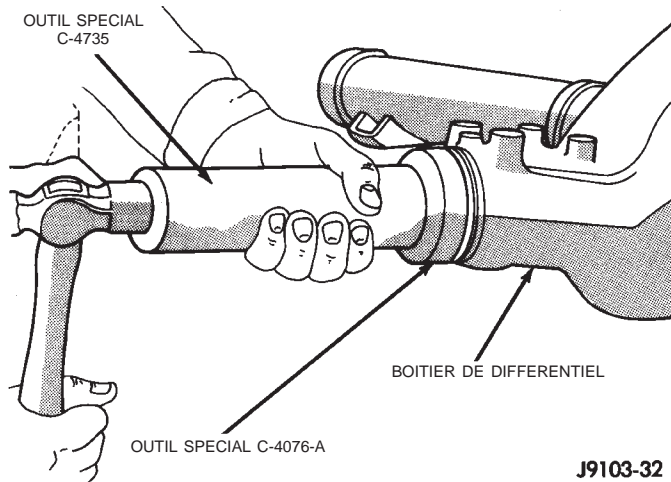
Pose de cuvette de roulement arrière de pignon
